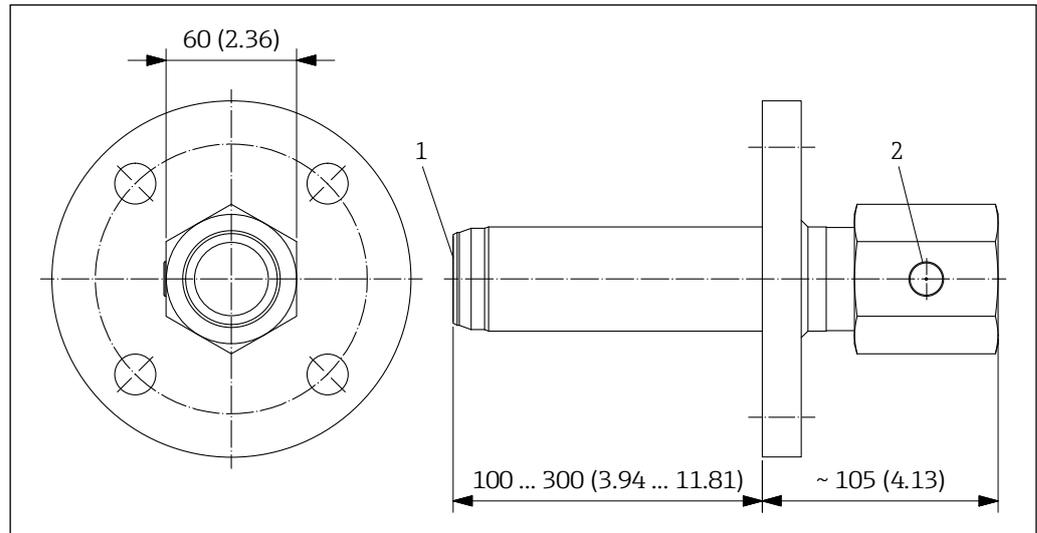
Dimensiones adaptador de inserción. Unidad de medida mm (in)
